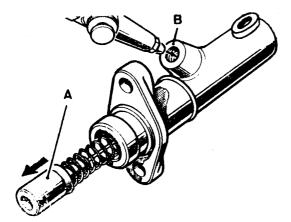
9 - Desmontaje del émbolo del cilindro principal.
